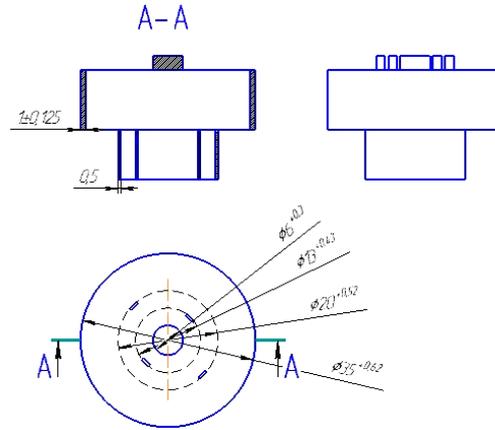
Емкостный 3-электродный коаксиальный датчик-крышка
